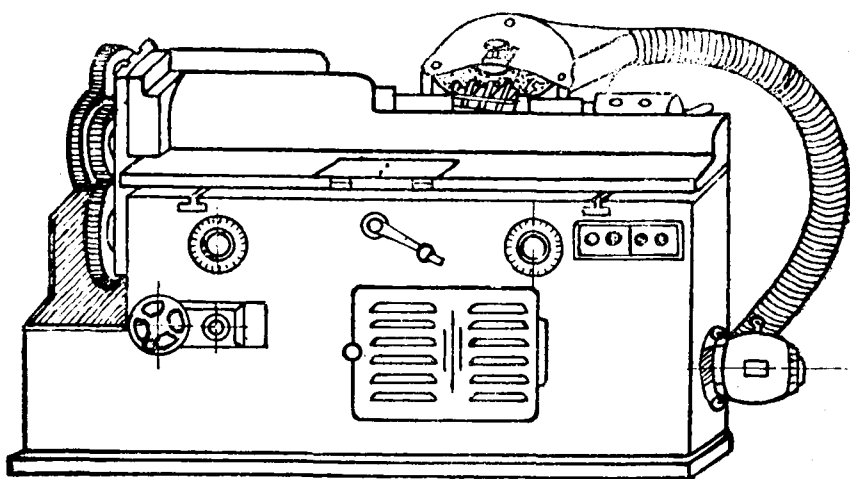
Заточка червячной фрезы на станке Клингельберг
